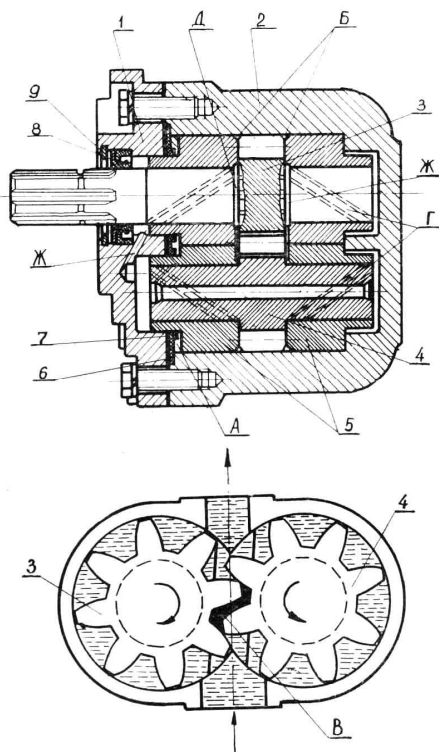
Конструкция шестеренного насоса с овальным корпусом: 1 – крышка; 2 – корпус; 3, 4 – шестерни; 5 – подшипники; 6 – манжета; 7 – прокладка; 8 – сальник самоподжимной; 9 – кольцо стопорное
